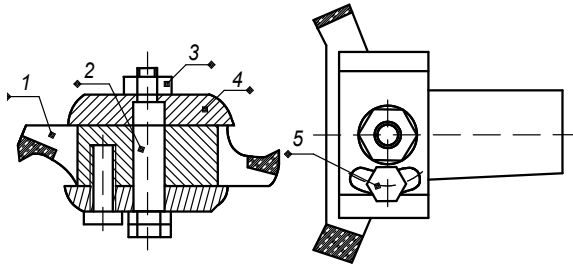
Регульована двопера фреза для обробки легких сплавів
